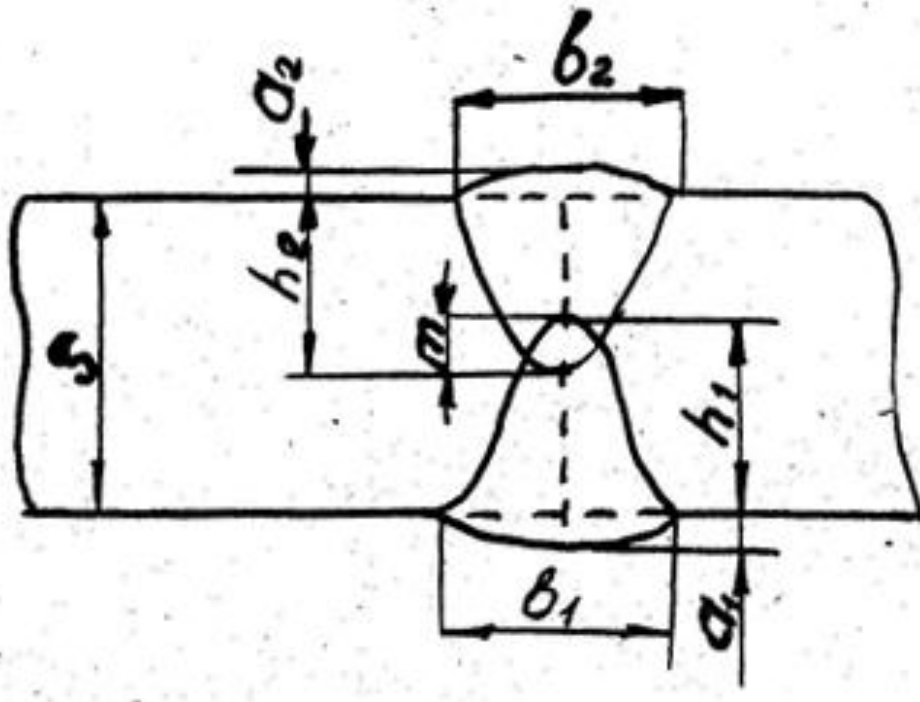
Геометричні розміри шва при двобічному зварюванні
